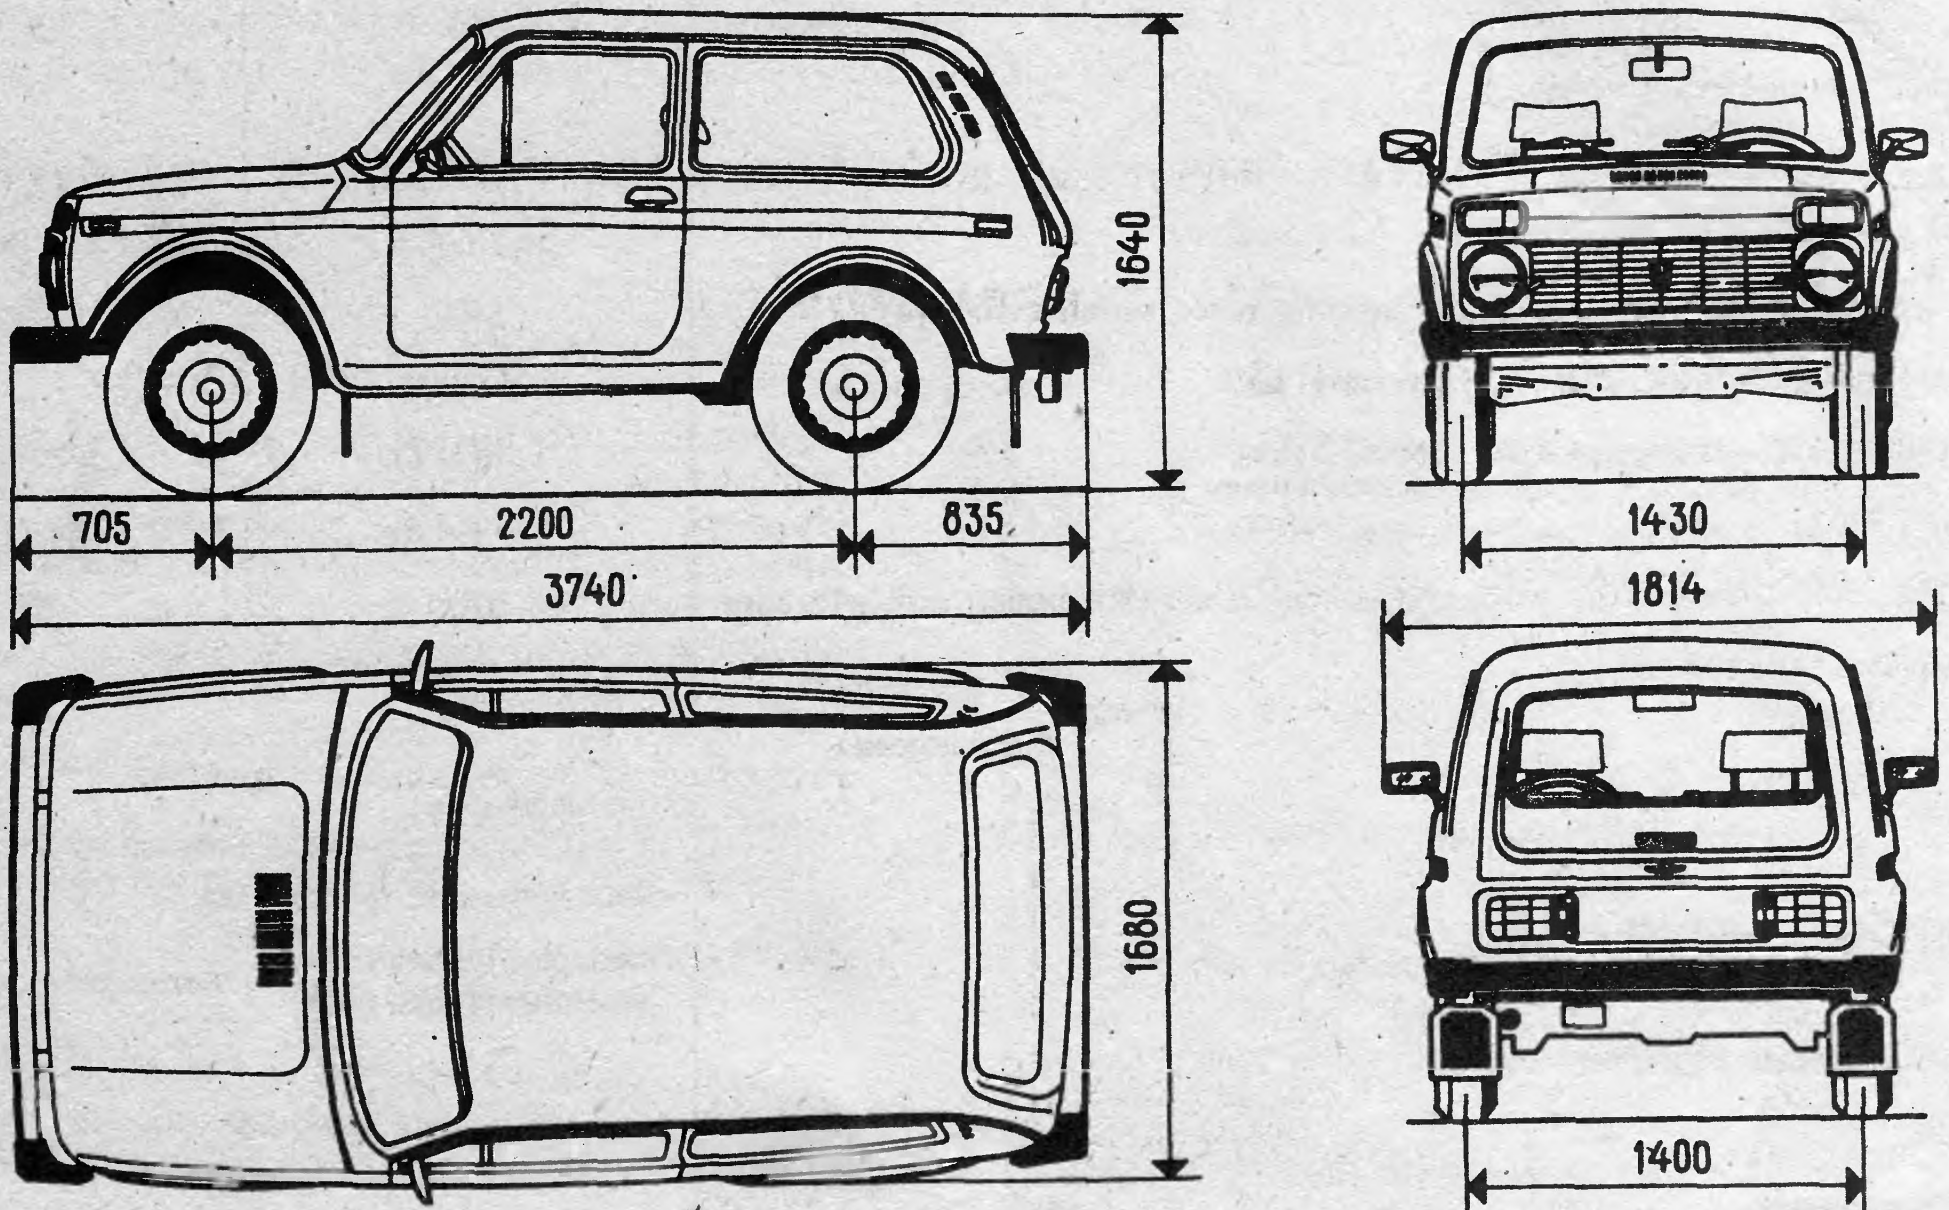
Основные габаритные размеры автомобиля ВАЗ-2121
